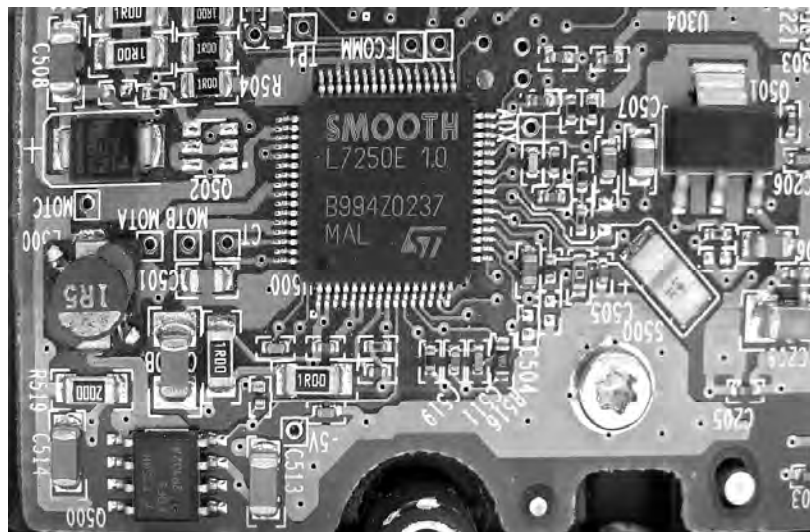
Внешний вид контроллера управления шпиндельным двигателем (SMOOTH L7250E 1.0) НЖМД Maxtor Diamond Max Plus 9 CALYPSO
